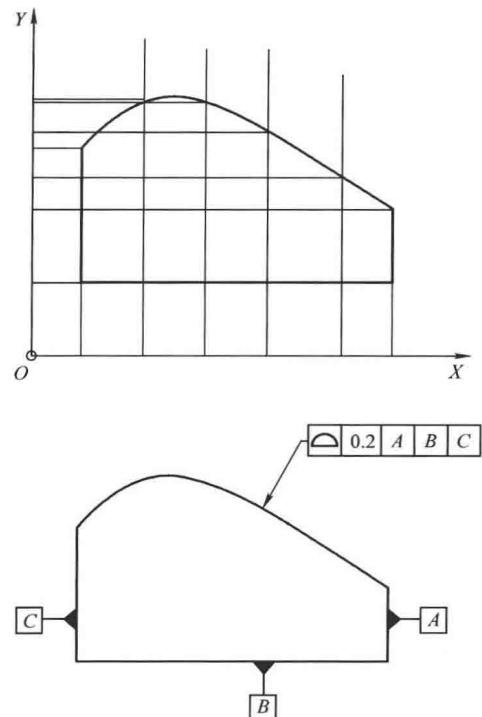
尺寸公差和几何公差对于异形特征的定义
